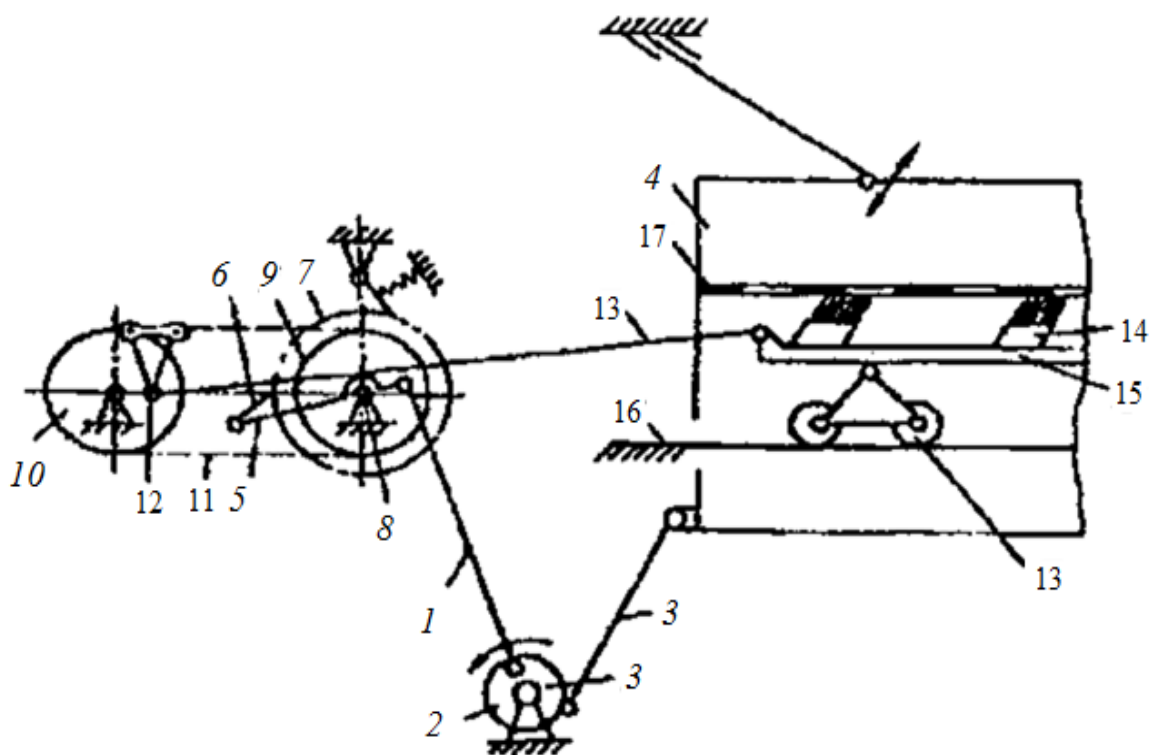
Совмещенный механизм привода решетного стана с механизмом очистки: 1 – шатун; 2 – кривошип; 3 – привод; 4 – решётный стан; 5 – рычаг; 6 – собачка; 7 – храповое колесо; 8 – вал; 9 – ведущая звёздочка; 10 – дополнительная звёздочка; 11 – цепь; 12 – кольцо; 13 – тяга; 14 – щётки; 15 – каретка; 16 – направляющие; 17 – решето
